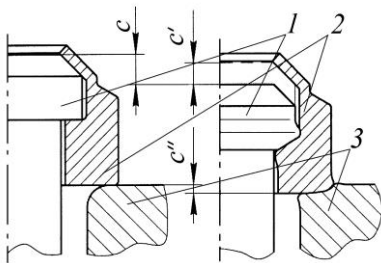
Зміна форми головки штока і стопорної шайби в процесі напрацювання ресурсу клапана
